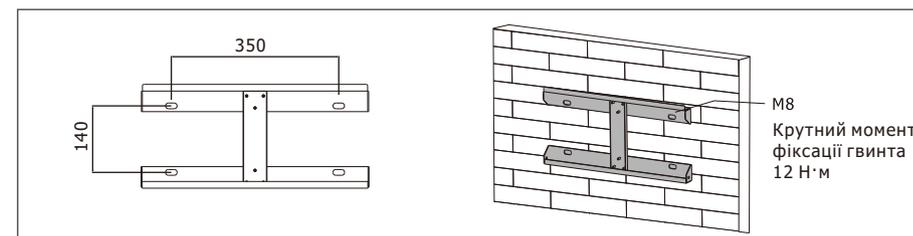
Інсталяція підвісної пластини інвертора
